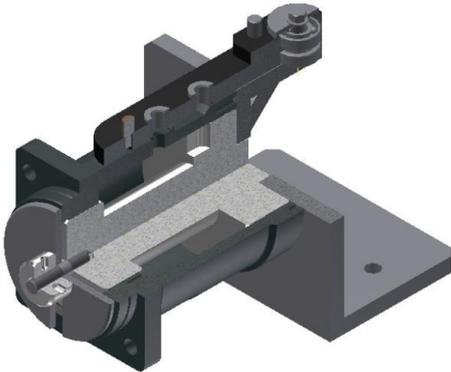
Приспособление для сверления дренажных отверстий корпуса А3-112/35.00.0001.01А аксиально-поршневого насоса
